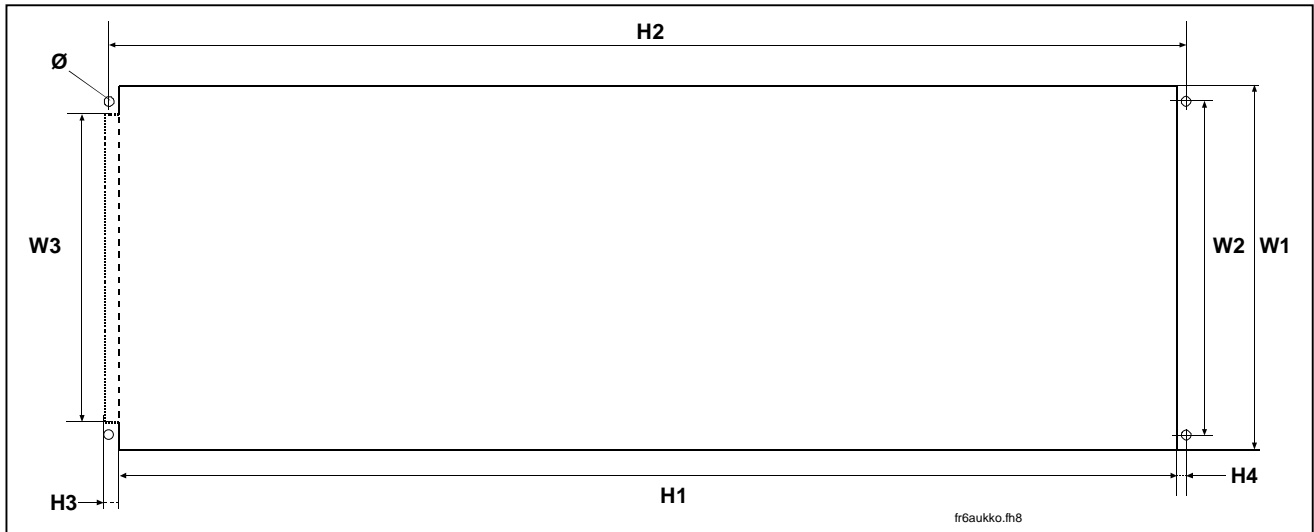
Abertura necessária para a montagem por flange, FR4 a FR6
